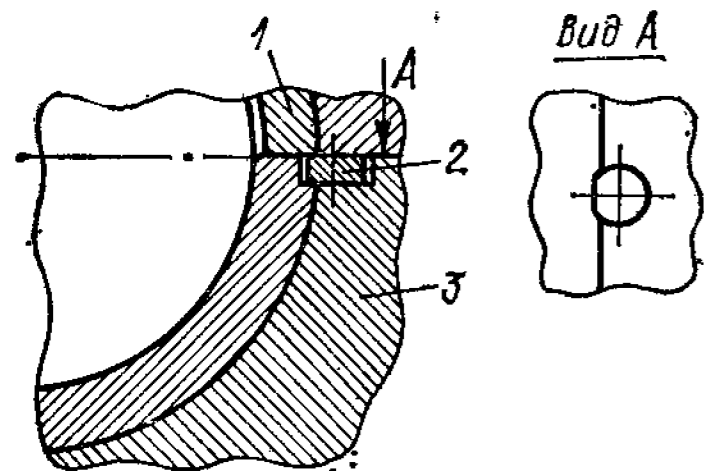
Фиксация вкладыша в разъемном корпусе подшипника скольжения:
